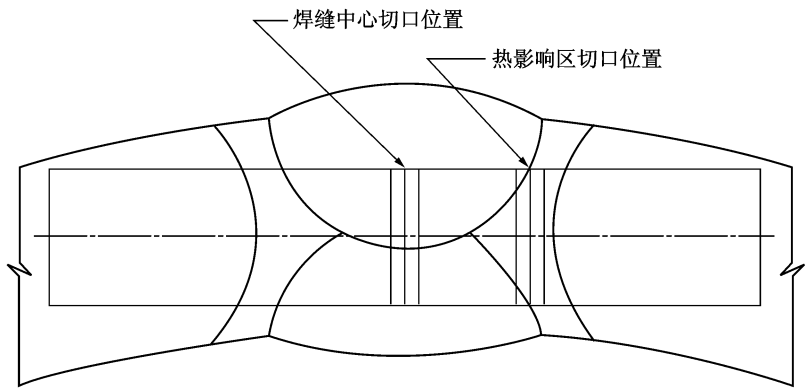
焊缝中心线和热影响区冲击试样缺口位置
